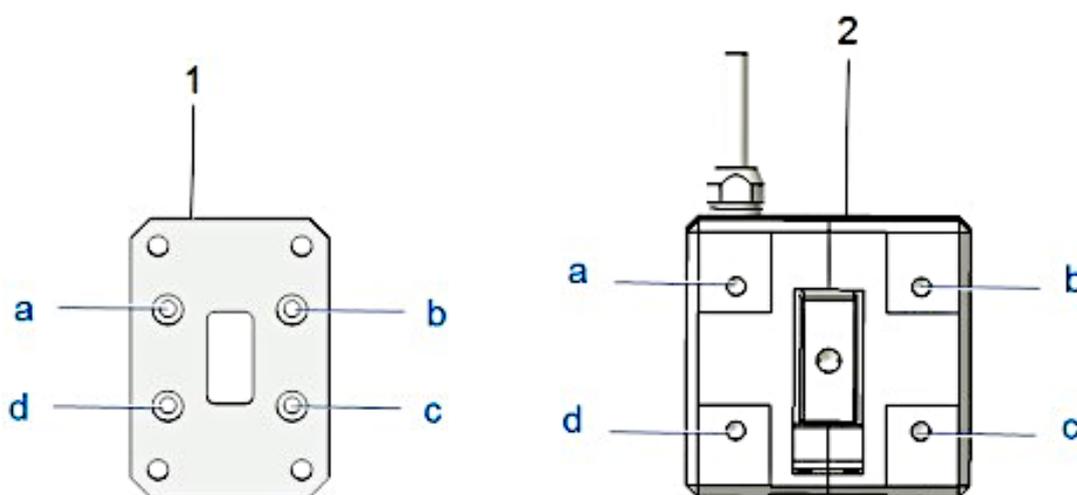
Übersicht der Montagebohrungen für Montageflansch B
